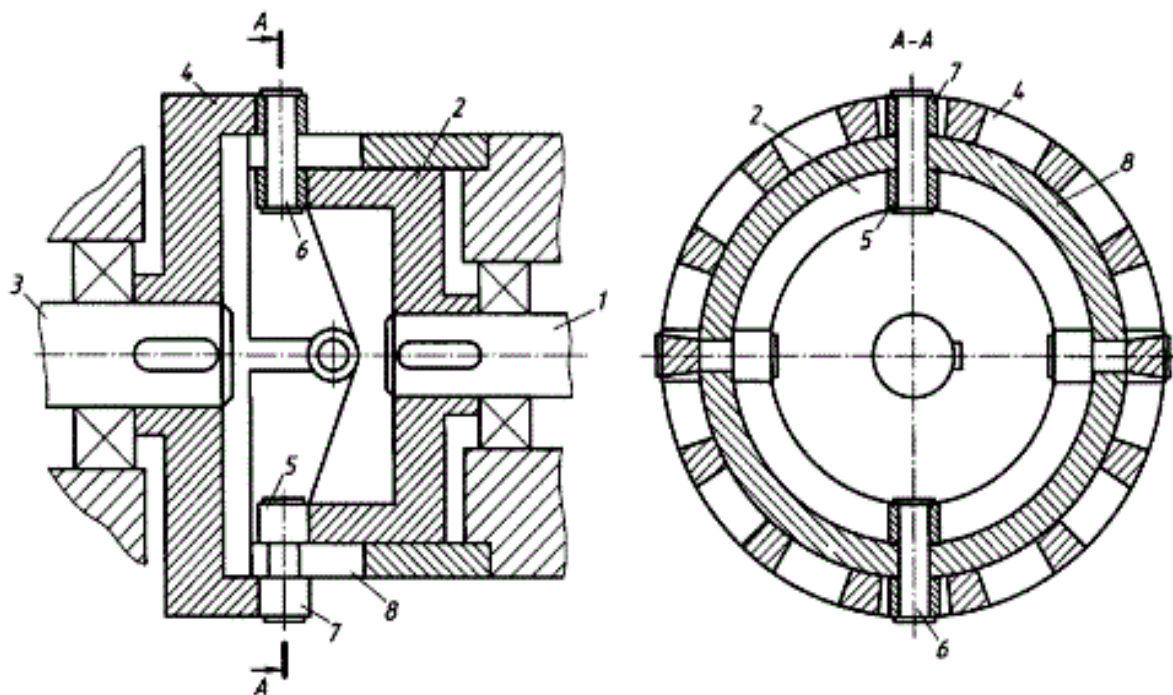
Торцевая зубчато-роликовая передача
